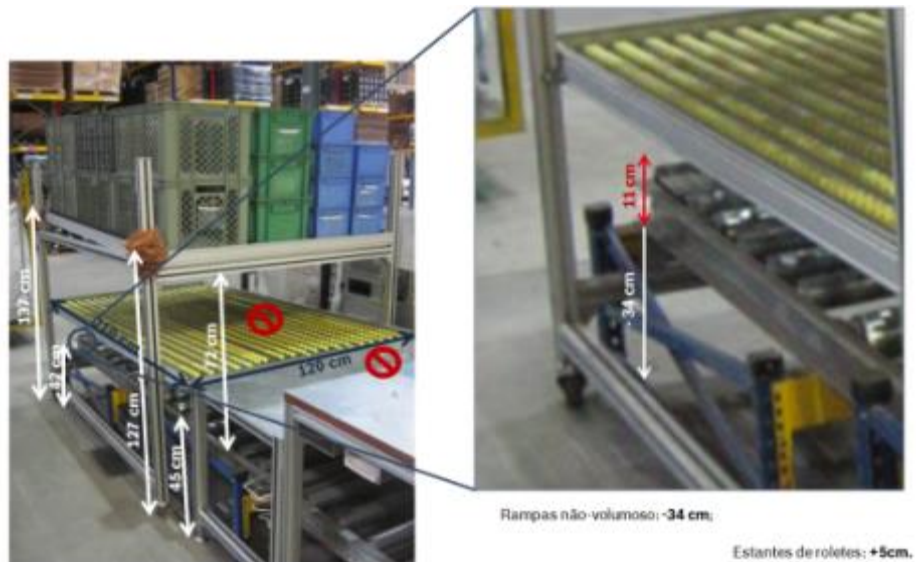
Proposta de alteração para rampa de colocação de caixas com material
